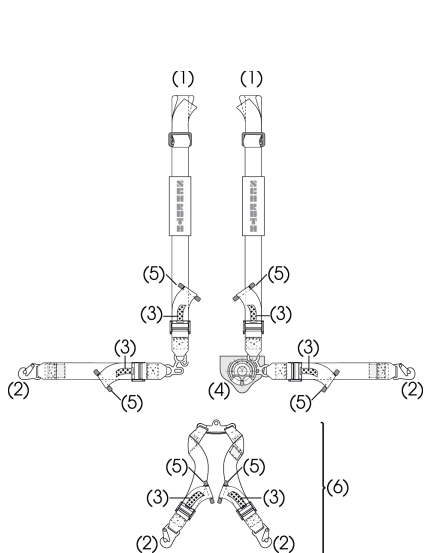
Partes de Sistema de cinturón ultraBELT X-TREME
